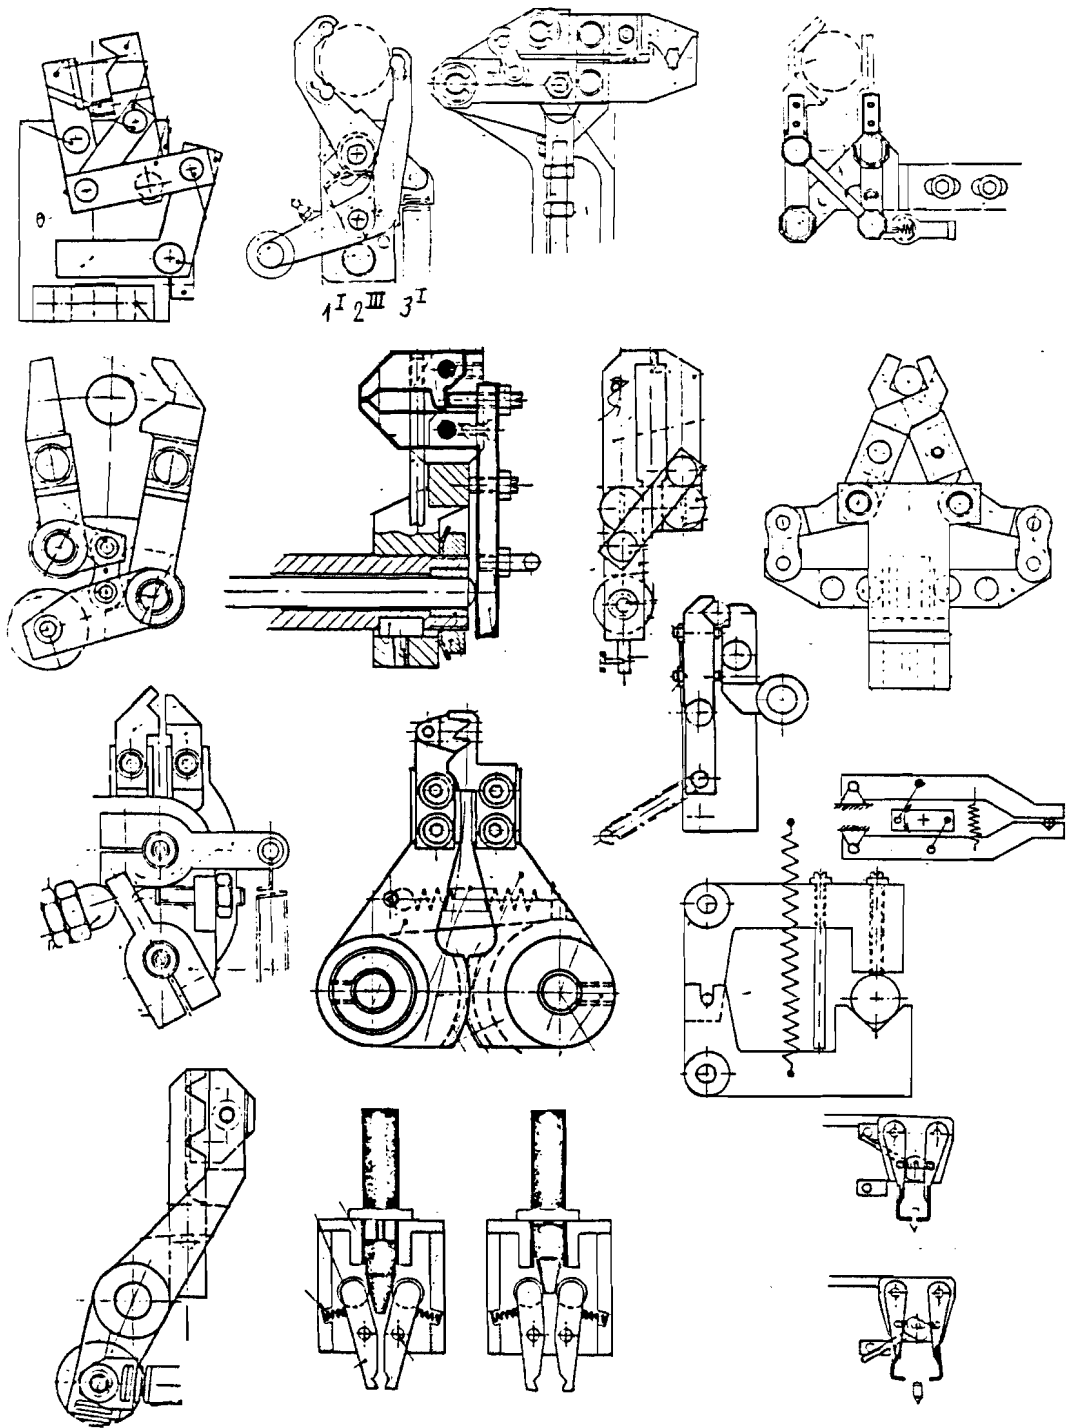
Voorbeelden van bestaande tangkonstrukties
